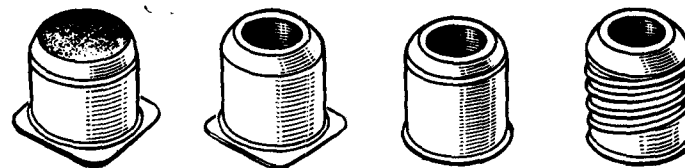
Стадии штамповки цоколей Е27-1 и готовый корпус цоколя.
